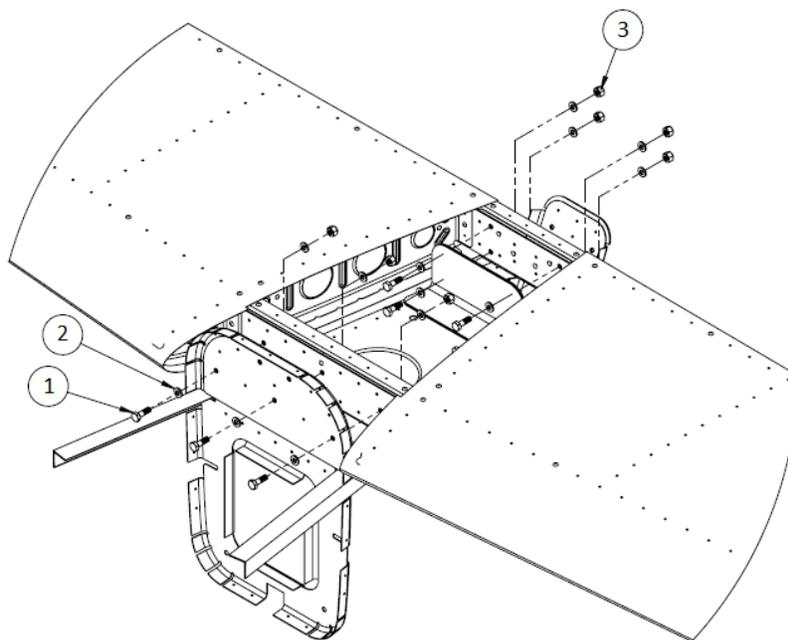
Instalação do Estabilizador Horizontal.
